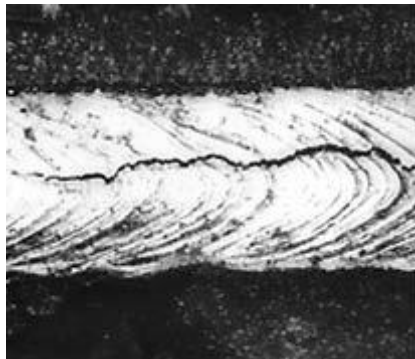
Indicación de soldadura tipo fisura.
